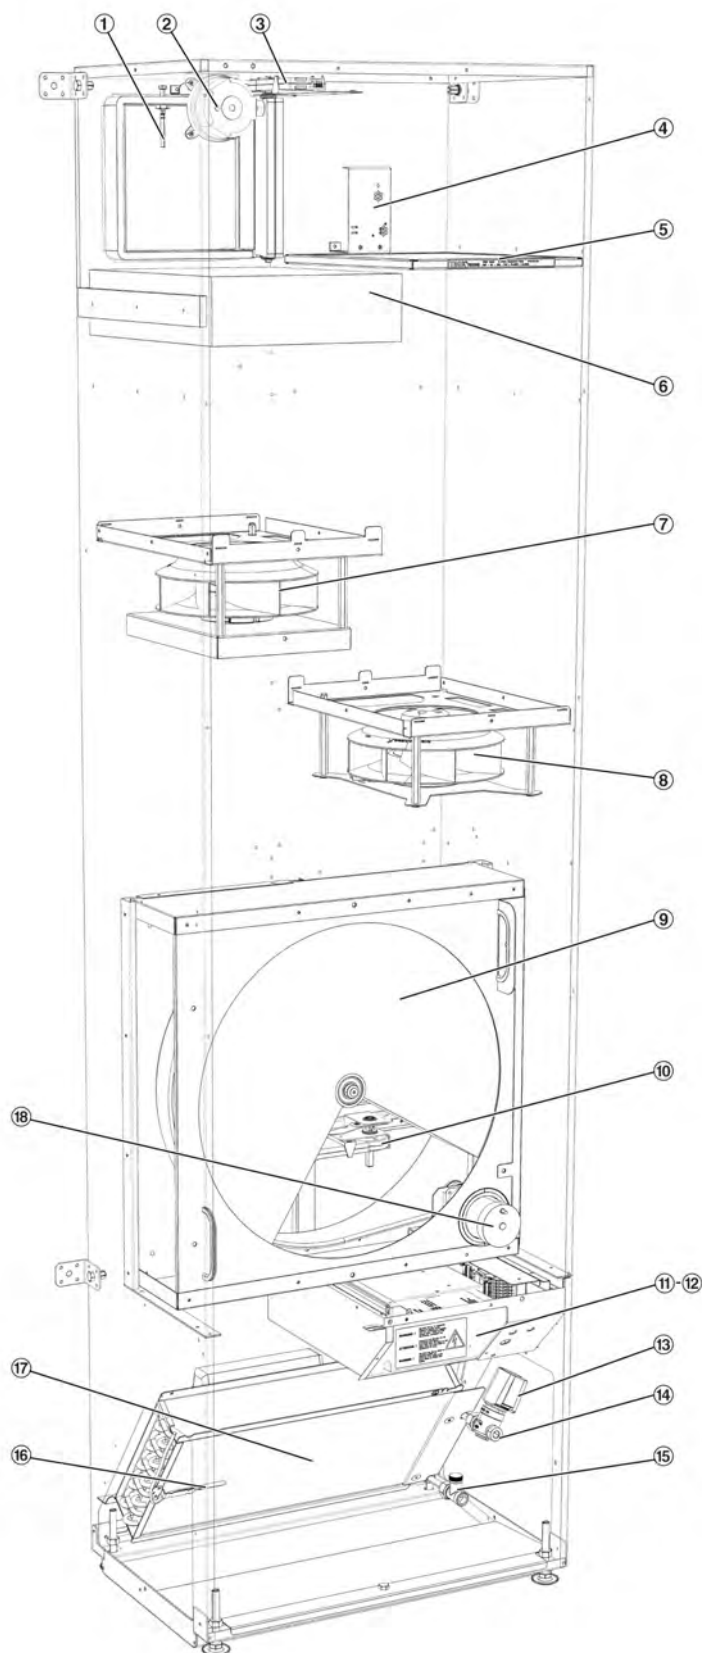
Lista części zamiennych SCHOOLAIR-V-HE
